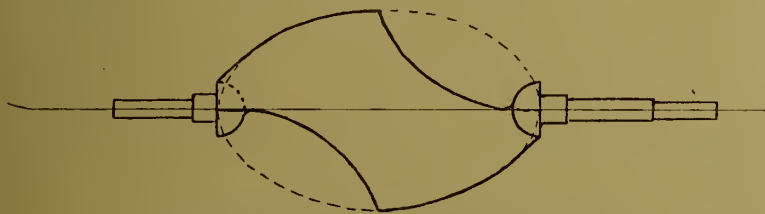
Grundform der Werner & Pfeleidererschen Knet- und Misch-Maschine.
